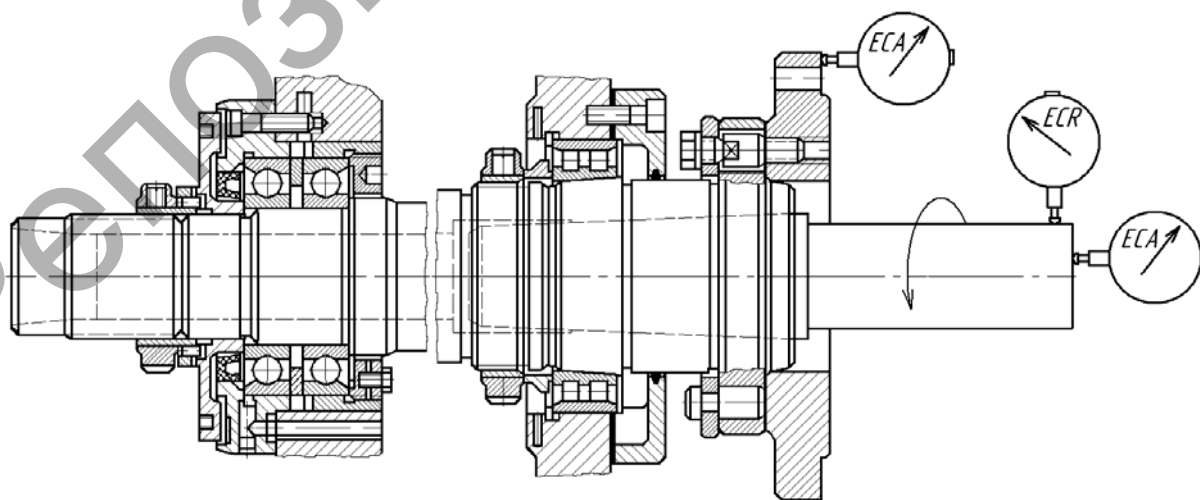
Проверка шпиндельного узла токарного станка на точность
